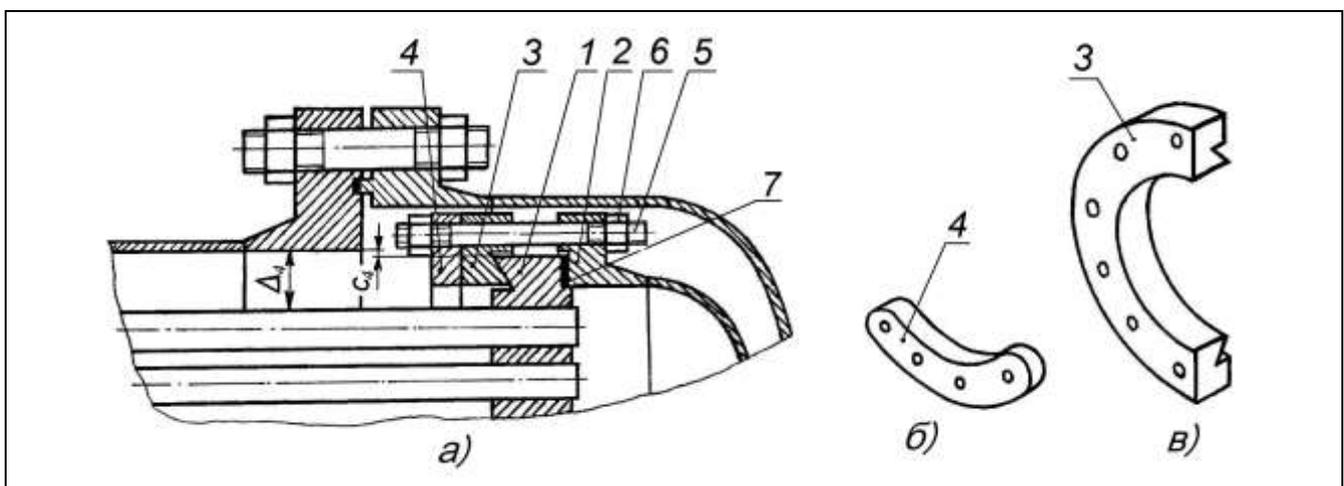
Плавающая головка с разрезным стяжным кольцом 3 и двумя дуговыми накладками 4: а) – общий вид плавающей головки; б) – внешний вид дуговой накладки 4; в) – внешний вид левой половины стяжного кольца 3 до начала сборки
